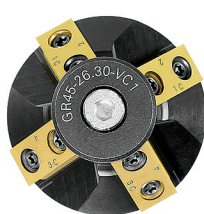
°-Fasen-Fräser mit 4 Schneiden und Führungsrolle, bestückt mit 4 Fasen-Wendeschneidplatten vom Typ D
